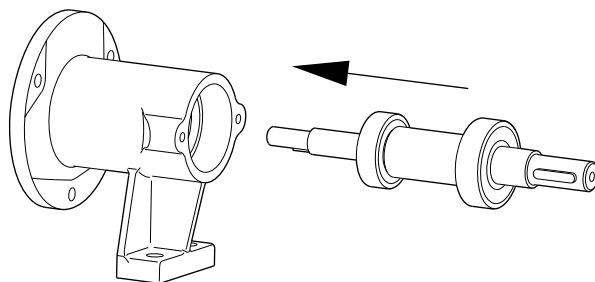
Установка вала с подшипниками в подшипниковый узел
